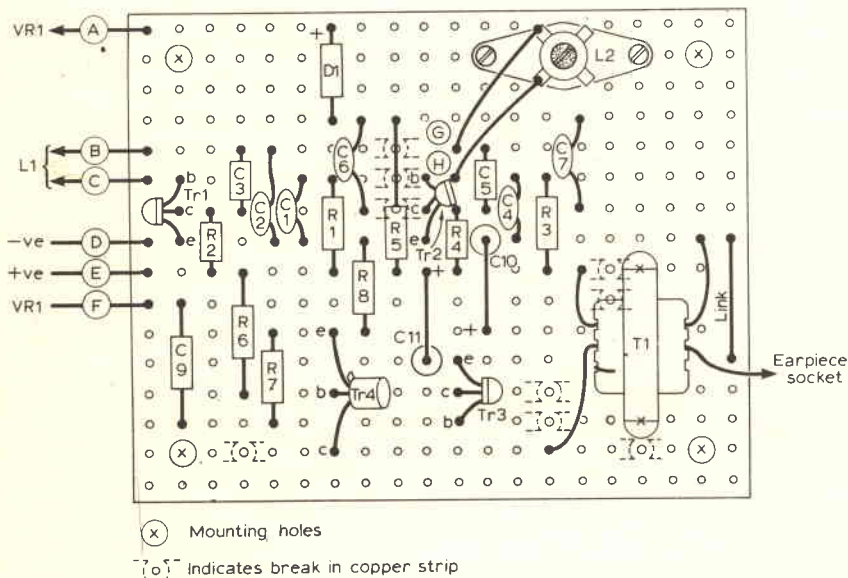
Disegno della basetta a circuiti stampati sulla quale possono essere applicati tutti i componenti della parte elettronica.
